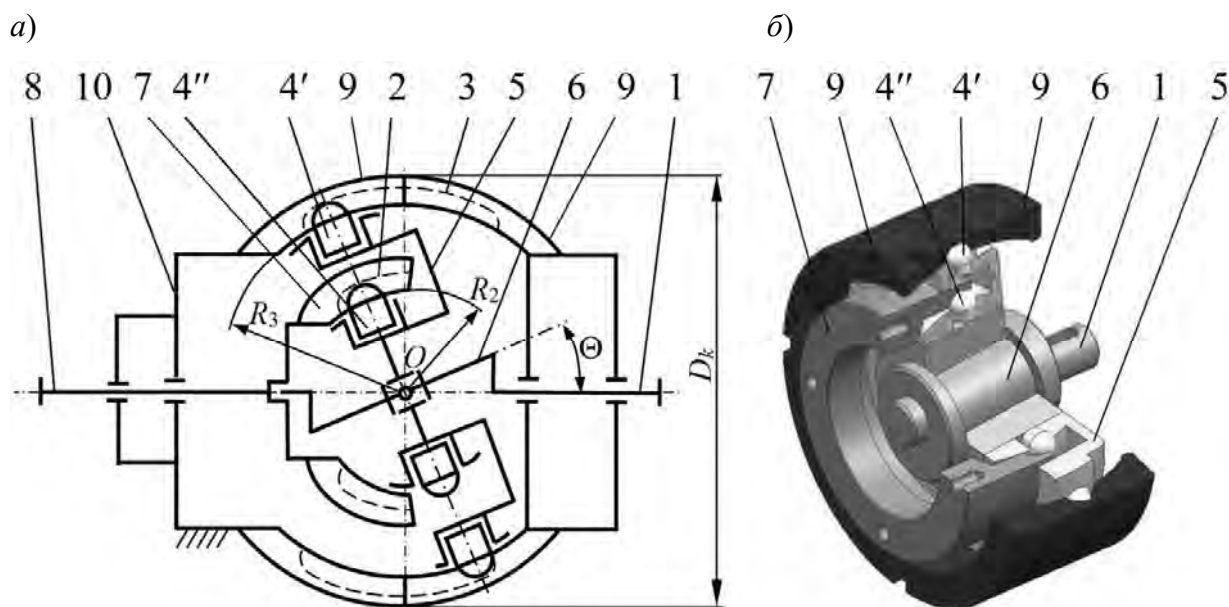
СРП с двухрядным сателлитом: а – кинематическая схема; б – общий вид; 1 – ведущий вал; 2 – беговая дорожка ведомого кулачка; 3 – беговая дорожка, образованная остановленными кулачками; 4' и 4'' – наружный и внутренний ряды роликов; 5 – сателлит; 6 – кривошип; 7 – ведомый (внутренний) кулачок; 8 – ведомый вал; 9 – остановленные (наружные) кулачки; 10 – корпус
